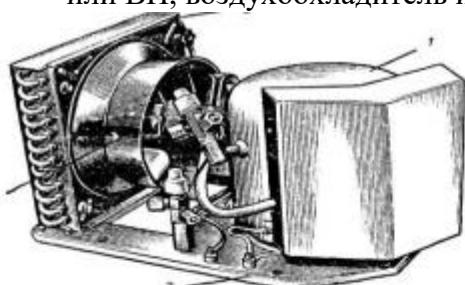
Холодильный агрегат ВС 400-1 [2]: 1 — герметичный компрессор; 2 — конденсатор; 3 — штампованная плита; 4 — диффузор
